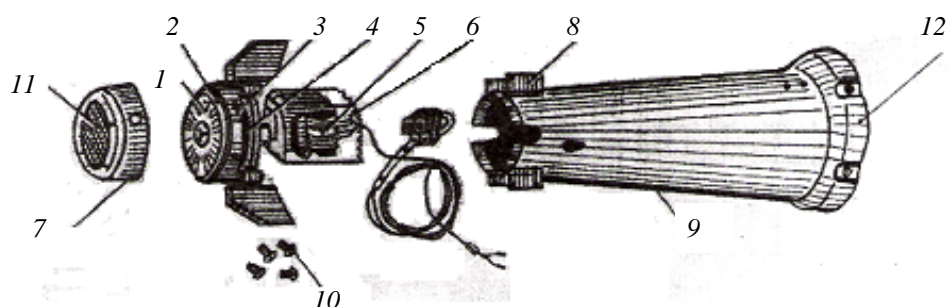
Блок рулевого привода (внешний вид): 1 – диск подвижный; 2 – диск неподвижный; 3 – основание; 4 – чашка; 5 – магнит управляющий; 6 – кожух; 7 – колпак; 8 – дестабелизатор; 9 – конус; 10 – винт; 11 – сетка фильтрующая; 12 – выступ
